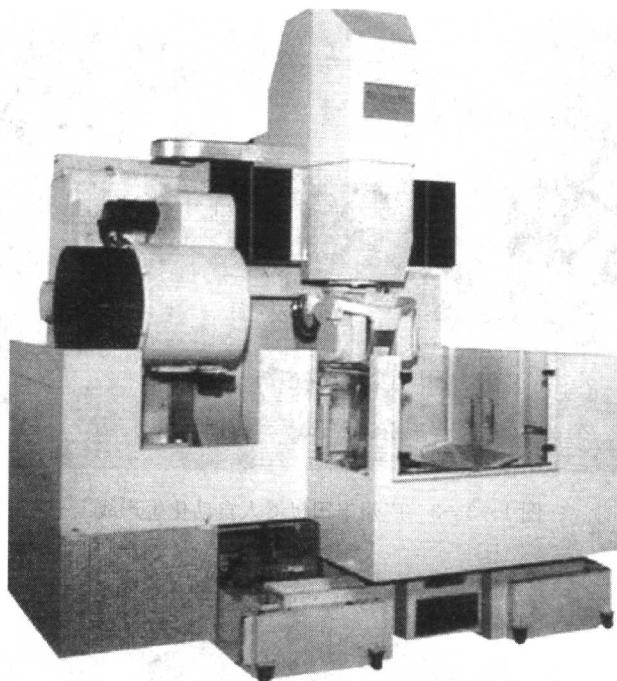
3—2 DIC—45/5 轴精密高速轮廓加工机床
